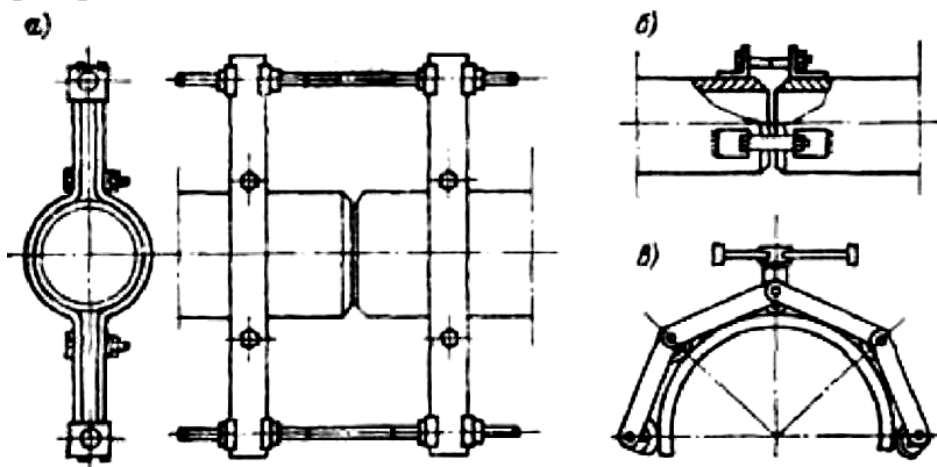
Приспособления для центровки труб: а – хомутового типа; б – стяжные уголки; в – безмоментный наружный центратор
